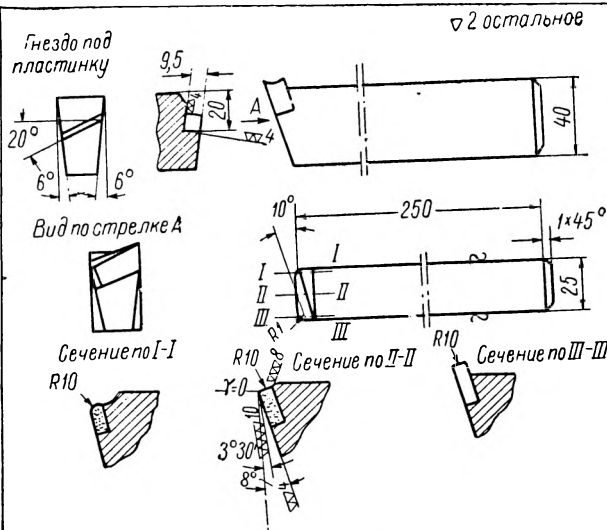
Чистовой резец конструкции И. Е. Савина.
